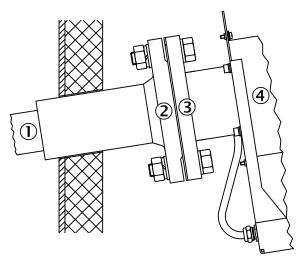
Montaggio del tubo di campionamento del gas sulla flangia di testa a saldare
